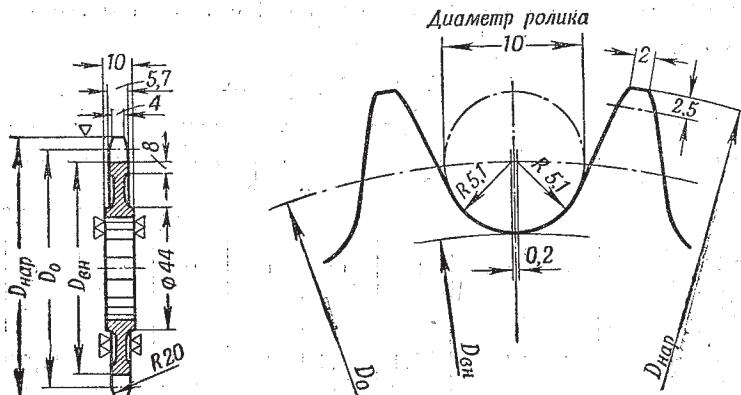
Звездочка цепной передачи для ИЖ-49 и ИЖ-350
